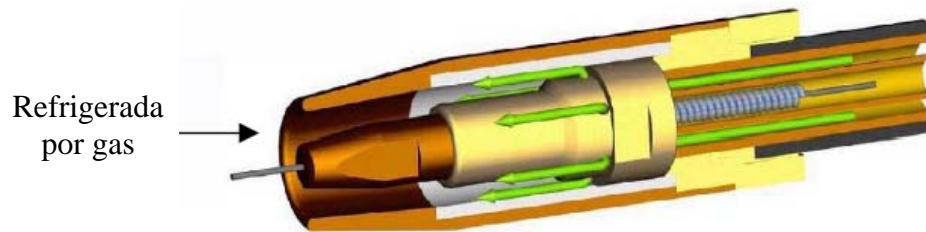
Sistema de refrigeración por aire para antorcha de soldadura.
